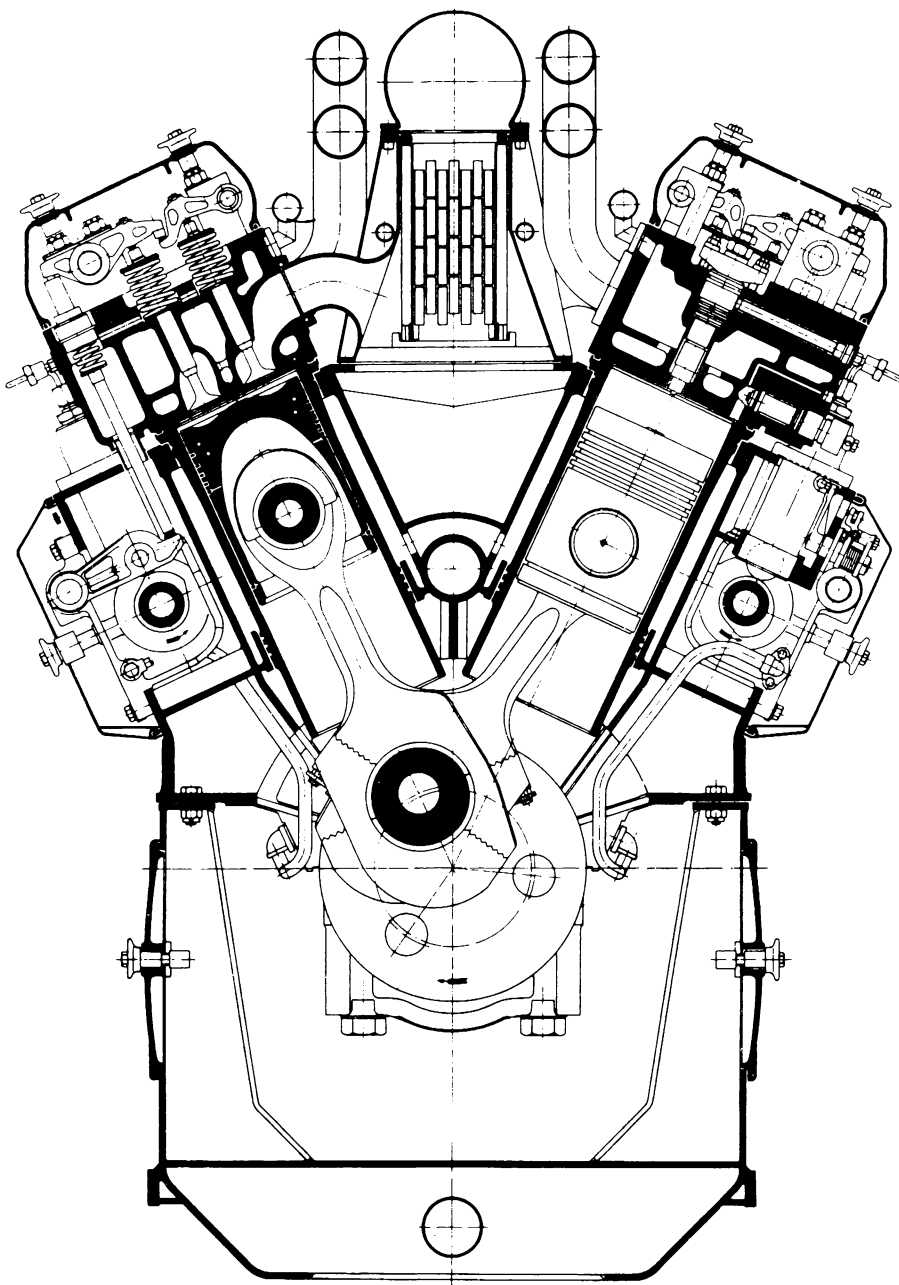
Bâti-cylindres en éléments assemblés par soudure.
